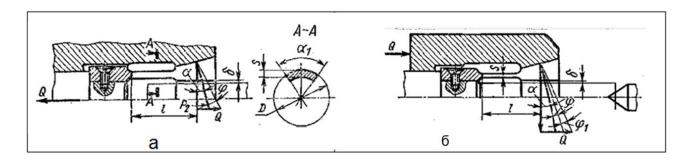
Установка заготовки в цанге: а – без осевого упора; б – с осевым упором,.
